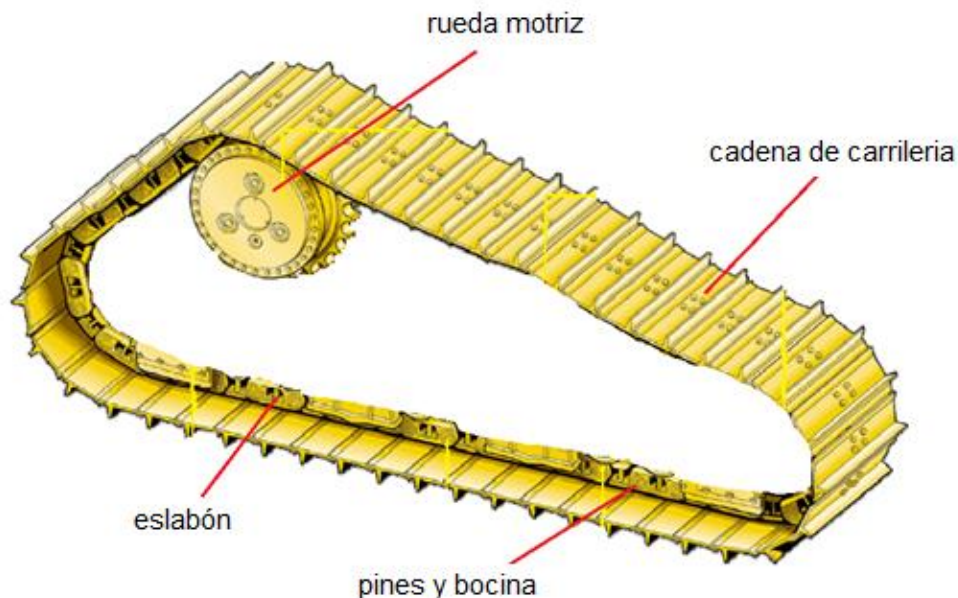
Partes de una cadena de carrilería en un tren de rodamiento.
